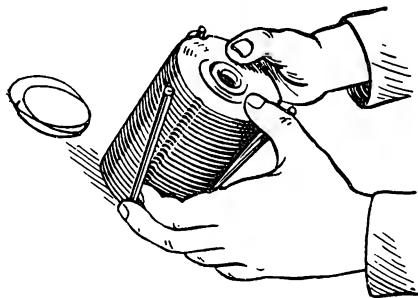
Сборка фильтрующего элемента тонкой очистки
